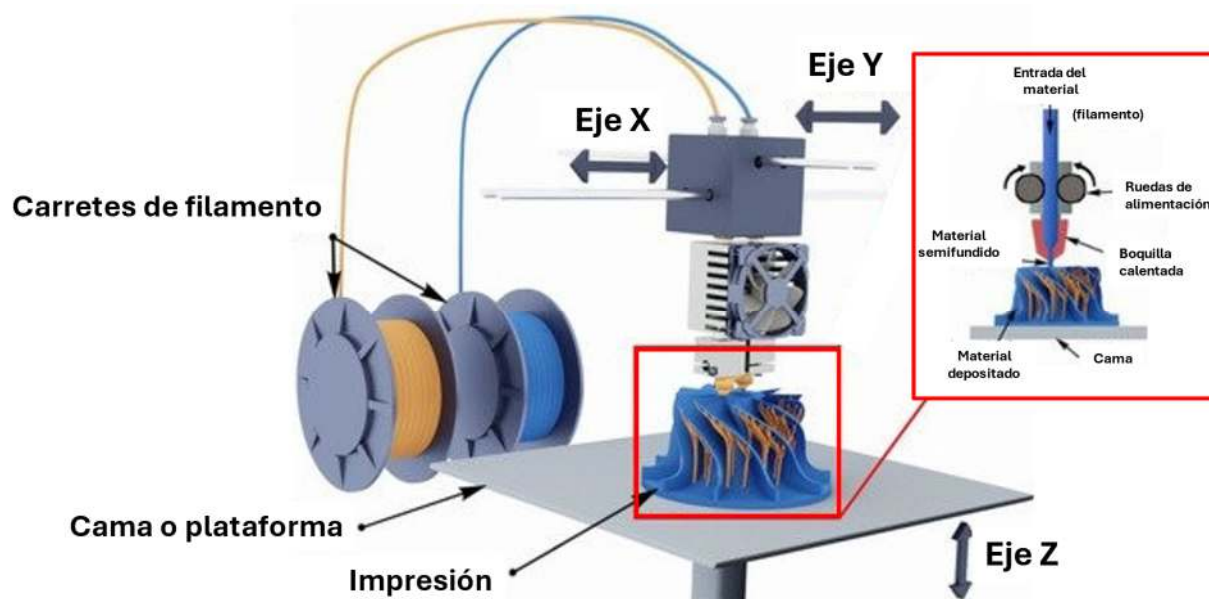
Esquema del proceso de impresión por Modelado por Deposición Fundida (FDM), adaptado de [68].
